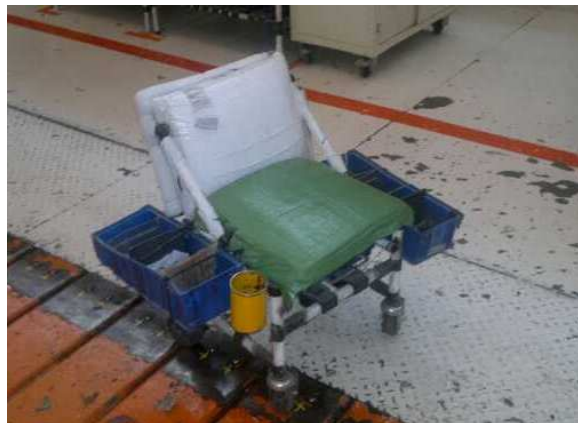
Foto Doll System puesto 9 lado izquierdo (9-LI). Fuente: Fotografía de los autores.
